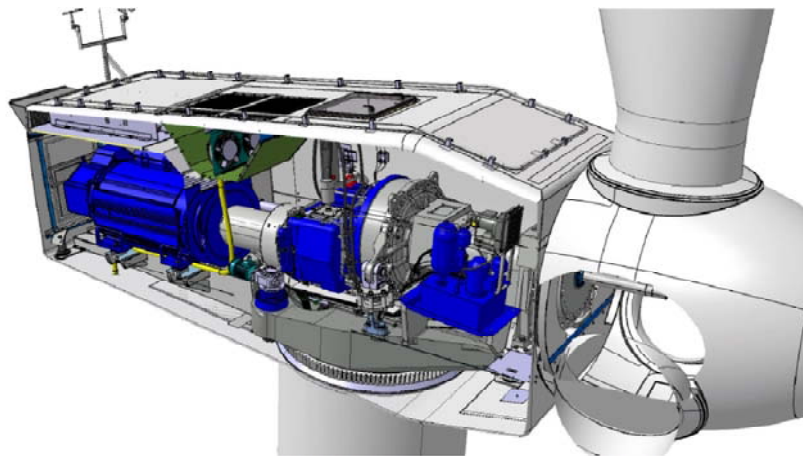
Vue latérale de Gamesa G52-850 kW
